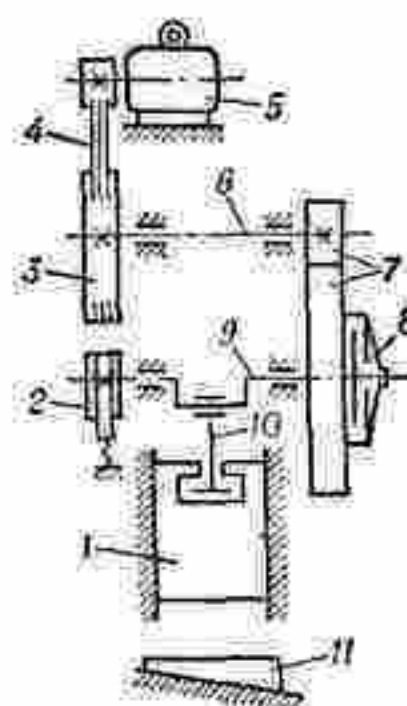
Кинематическая схема кривошипного пресса: 1 — ползун; 2 — тормоз; 3 — маховик; 4 — клиноремённая передача; 5 — электродвигатель; 6 — передаточный вал; 7 — зубчатая передача; 8 — муфта; 9 — кривошипный вал; 10 — шатун; 11 — плита для крепления матрицы штампа.
